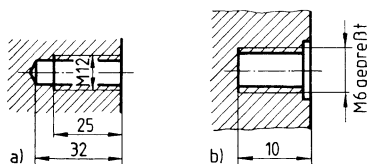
Gewindegrundlöcher, -länge (nutzbare) für
